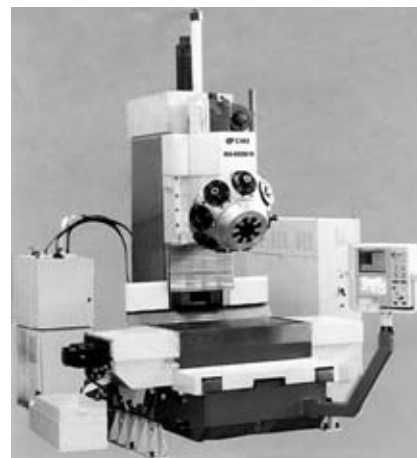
Вертикально-фрезерный станок МА-655 А14 с ЧПУ и автоматической сменой инструмента
